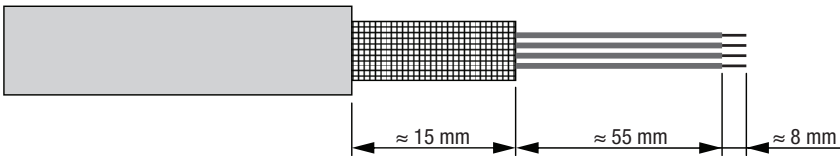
Confección del cable para el módulo de bornes MK 300
